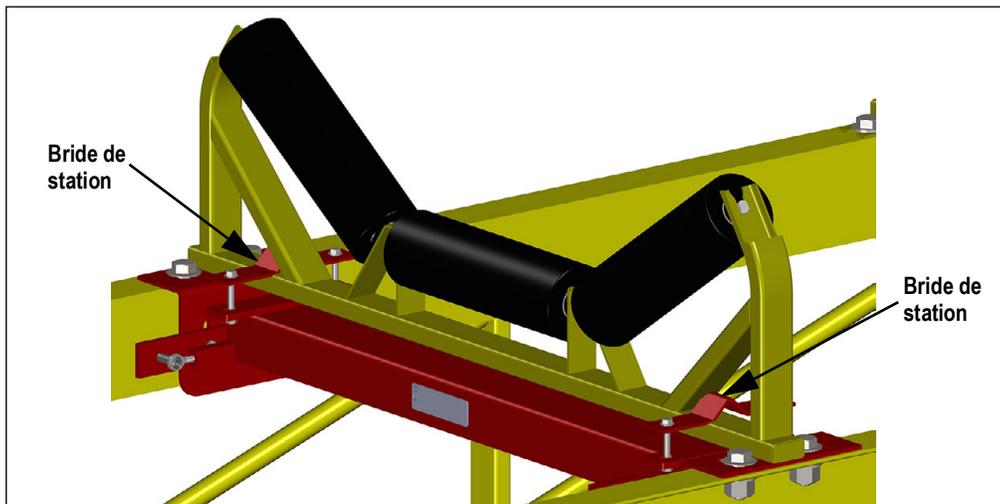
Installez la station rouleaux sur la barre peseuse 711
